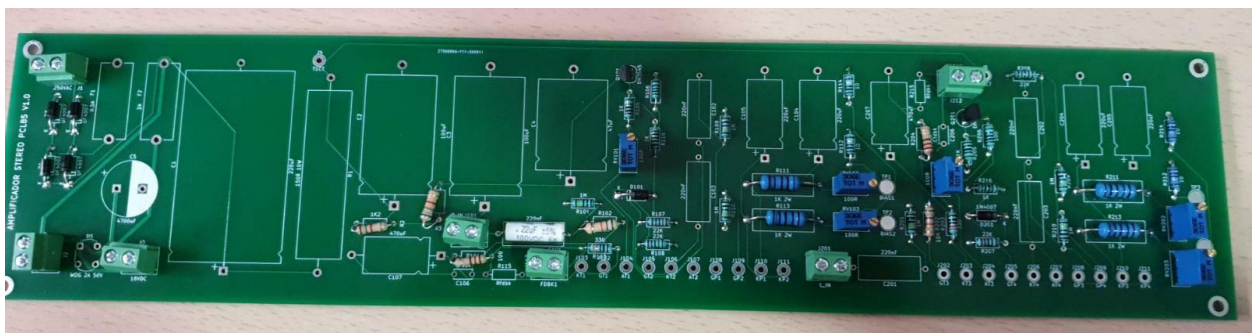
Componentes de mayor tamaño soldados al PCB.
